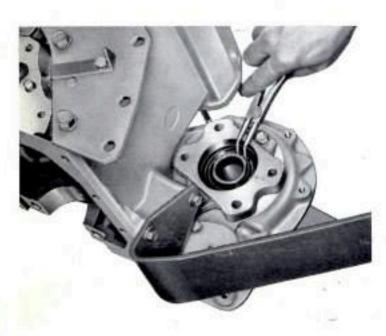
Smontaggio del motore: viene tolto l'anello elastico di ritegno ingranaggio comando pompa iniezione.
